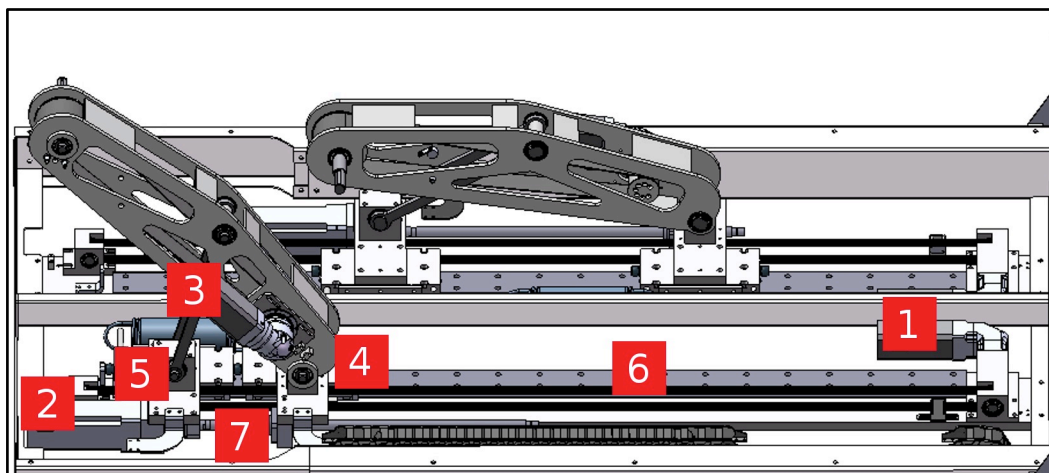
Meccanismo di movimento in tre dimensioni del G-EO. I componenti sono numerati come segue: 1. Motore principale; 2. Motore relativo; 3. Motore per l'angolazione del piede; 4. Slitta principale; 5. Slitta relativa; 6. Guida lineare; 7. Vite.
